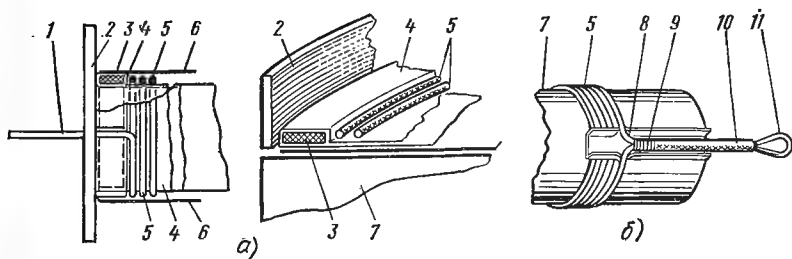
Намотка многослойной цилиндрической обмотки из круглого провода:
